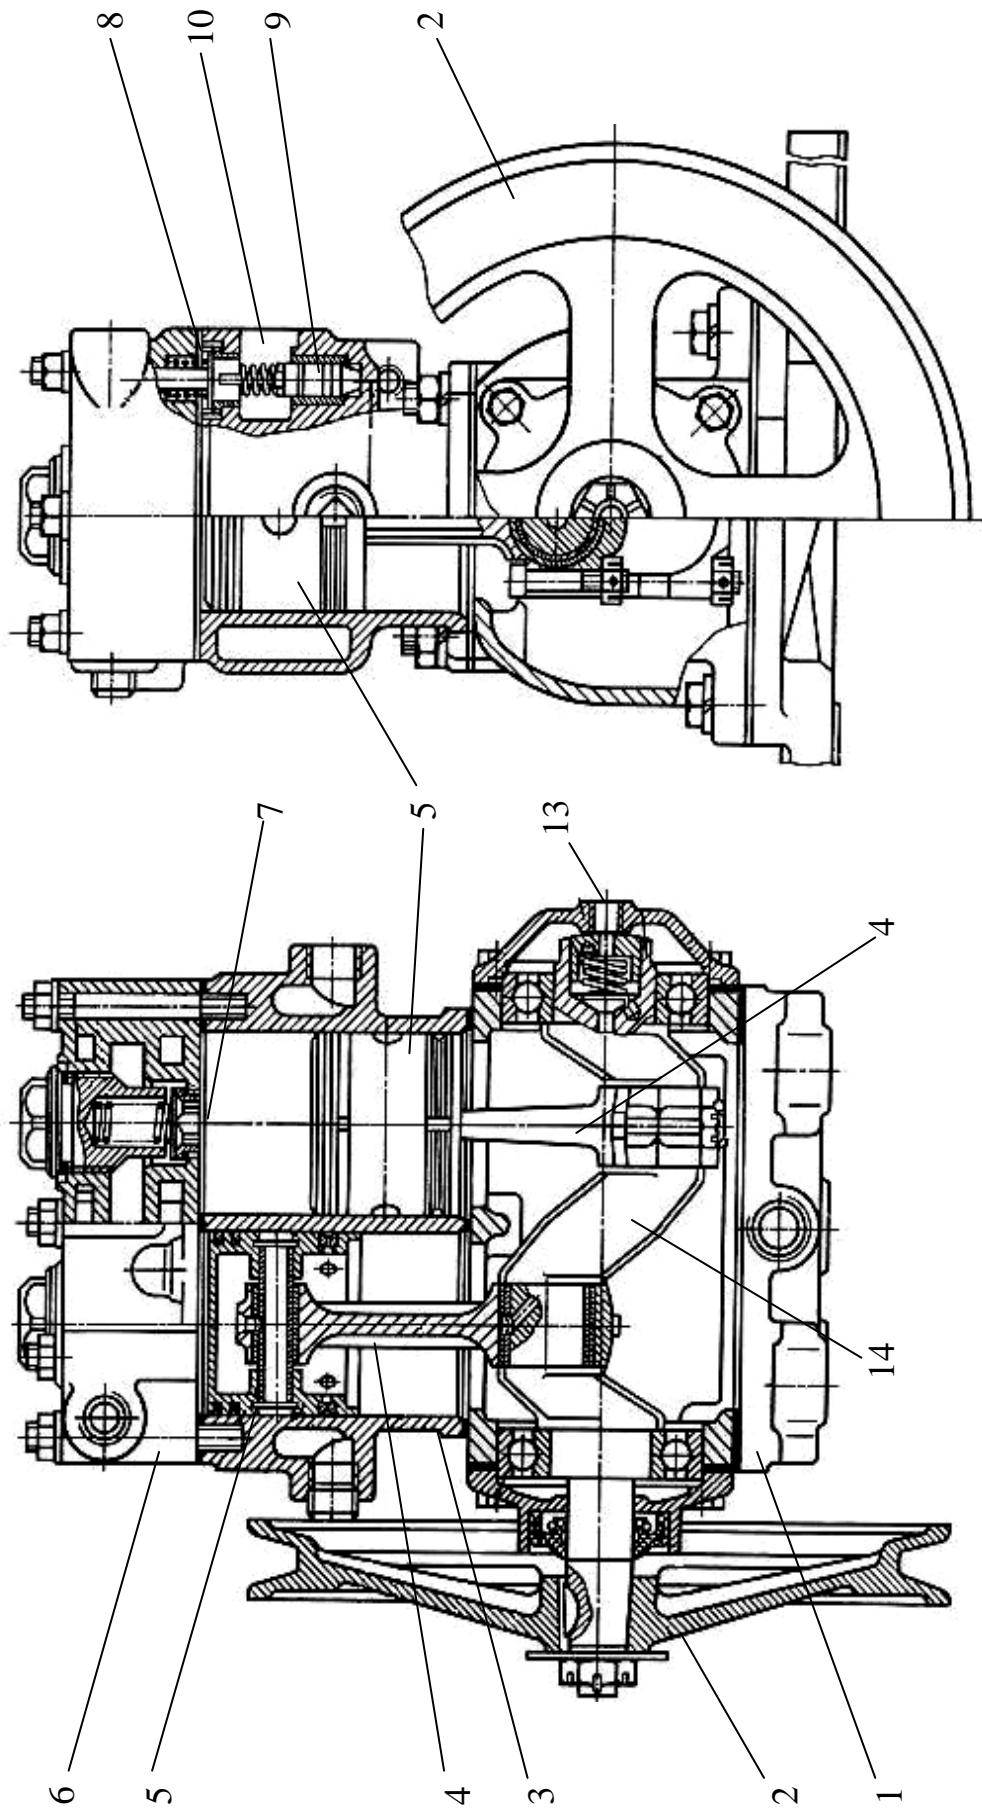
Компрессор: 1 – картер; 2 – шкив; 3 – блок цилиндров; 4 – шатун; 5 – поршень; 6 – головка блока; 7 – нагнетательный (выпускной) клапан; 8 – впускной клапан; 9 – плунжер регулятора давления; 10 – впускной канал; 13 – отверстие подвода масла из системы смазки двигателя; 14 – коленчатый вал
